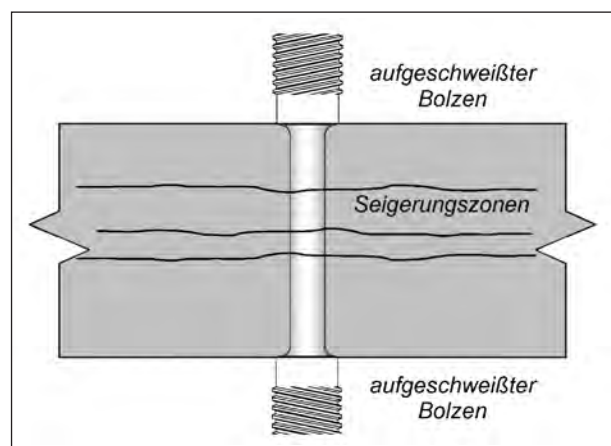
Rundprobe für Zugversuch (Beispiel)
